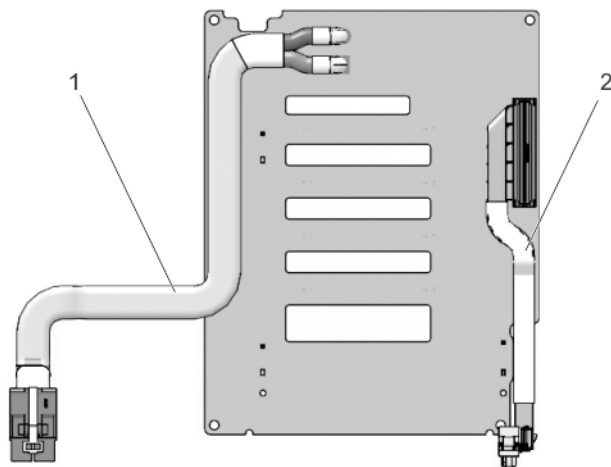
Fond de panier SAS/SATA (x4) de 2,5 pouces : vue arrière
